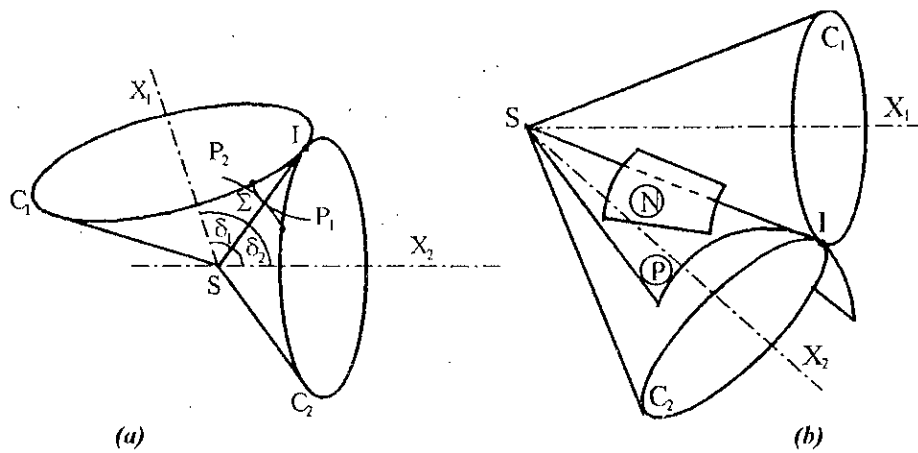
Méthodes de taillage des engrenages spiro-coniques [55].
